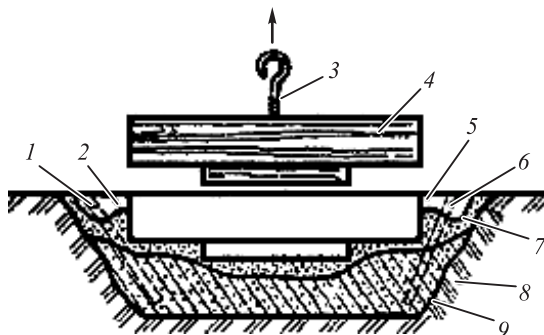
Технологический процесс изготовления открытой формы по мягкой постели: 1 – вентиляционный канал; 2 – приемная чаша; 3 – подъем; 4 – модель; 5 – питатель; 6 – литниковая чаша; 7 – облицовочная формовочная смесь; 8 – почва формовочного плаца; 9 – наполнительная формовочная смесь
